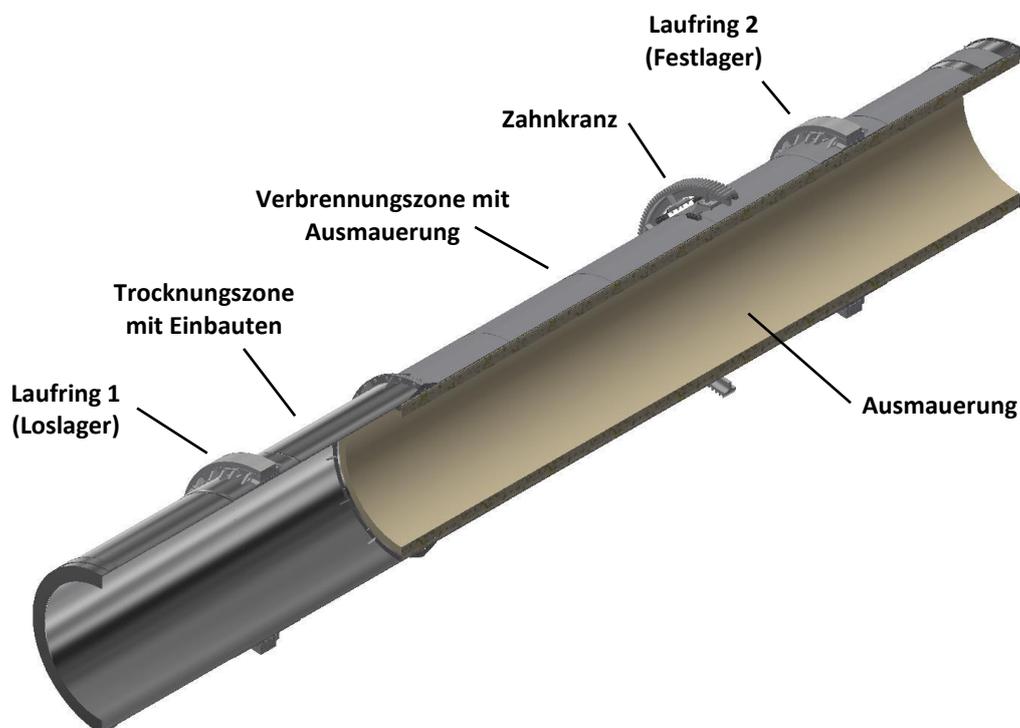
Drehrohr mit Ausmauerung o. Einbauten
